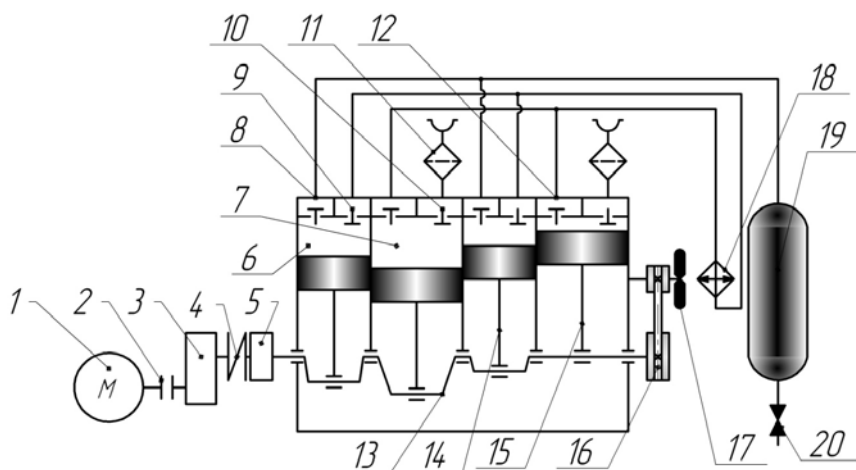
Принципиальная схема компрессорной станции на базе поршневого компрессора
